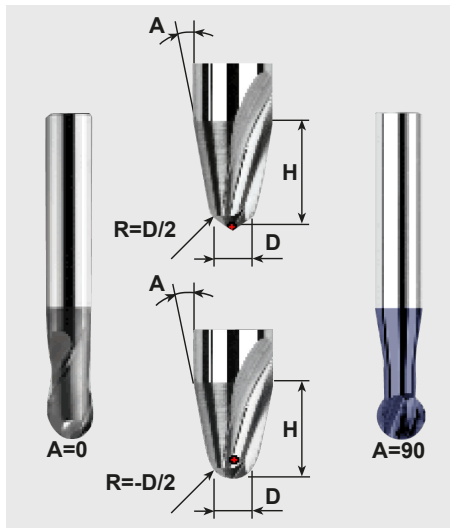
Werkzeugbeschreibung TOOL/MILL zylindrischer oder Kegelfräser mit optionalem Eckenradius
